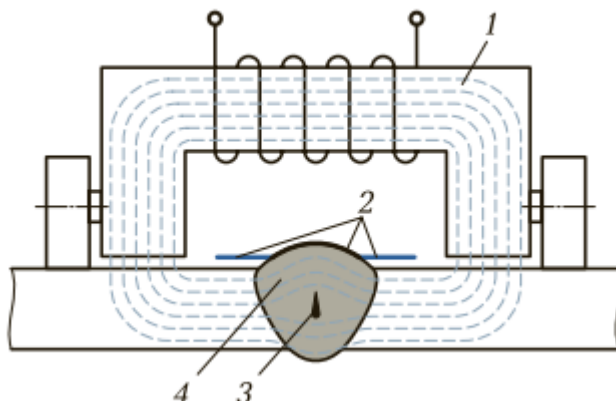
Схема магнитографического контроля: 1 — намагничивающее устройство; 2 — магнитная пленка; 3 — дефект; 4 — сварной шов
